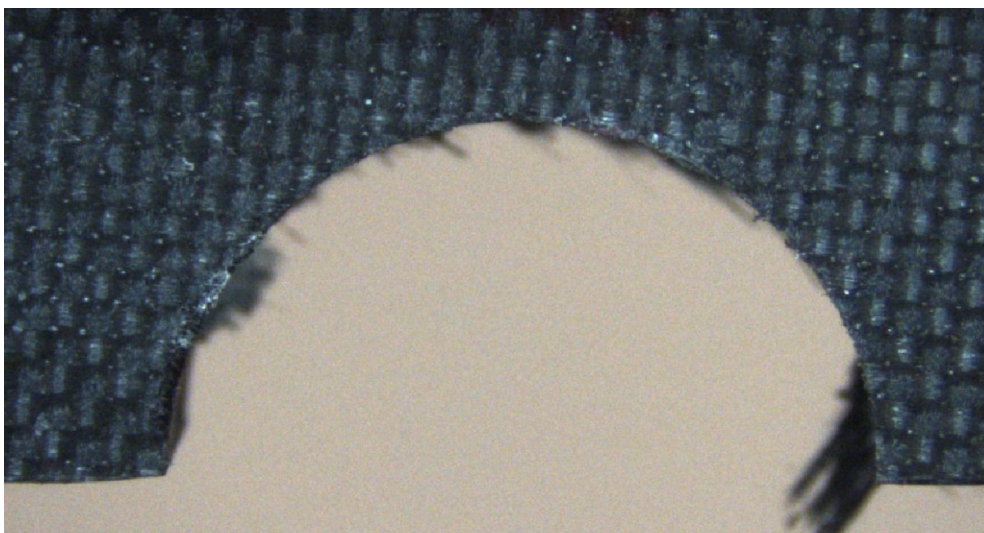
Varianta H – Spodní vrstva - Sousedně
